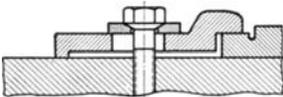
Spanneisen mit Dreipunktauflage (rechts 2 Wölbungen).
